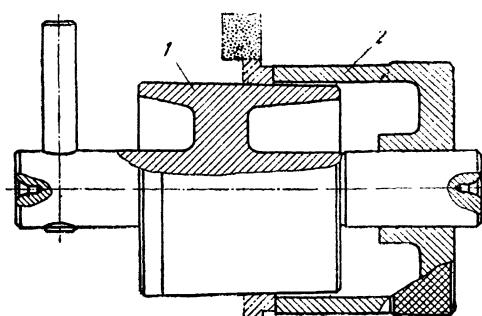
Жесткая конусная оправка для шлифовки колец.
